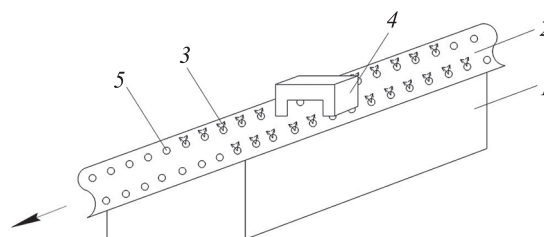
Схема работы устройства с тонкой газовой прослойкой: 1 — пневмокамера; 2 — рабочая поверхность устройства (например, в виде ленточного полотна); 3 — газовая прослойка; 4 — деталь; 5 — газоподводящие отверстия
